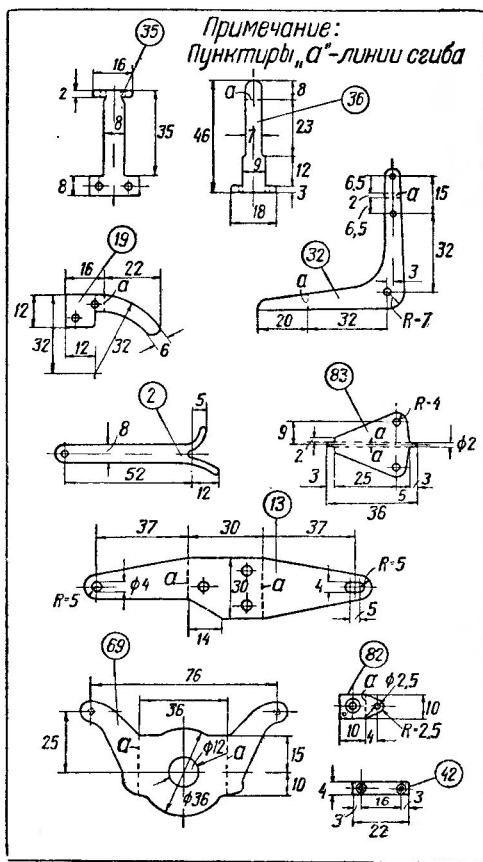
Мелкие детали автомата, изготовленные из листового металла.
